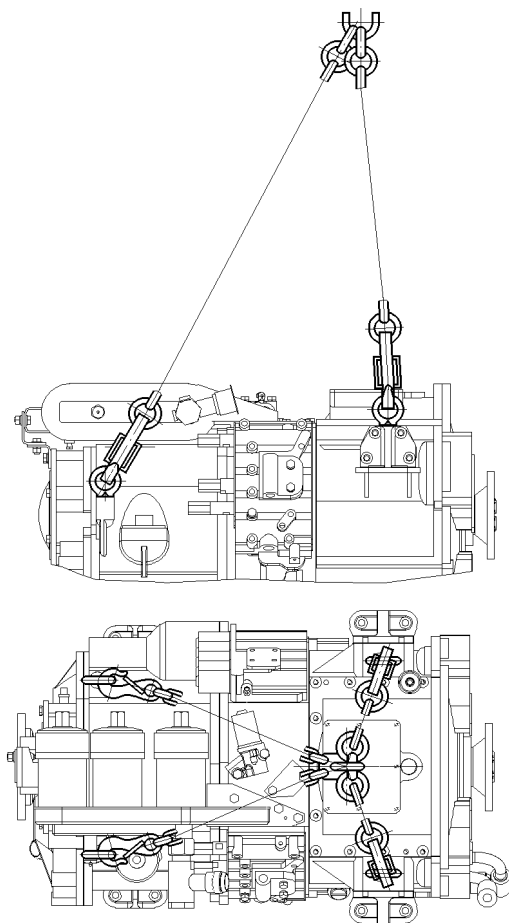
Приспособление для снятия и установки гидромеханической передачи
